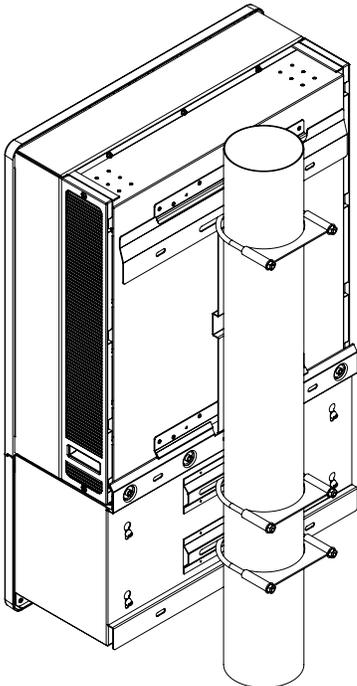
Montaje en postes: vista trasera con el inversor instalado
